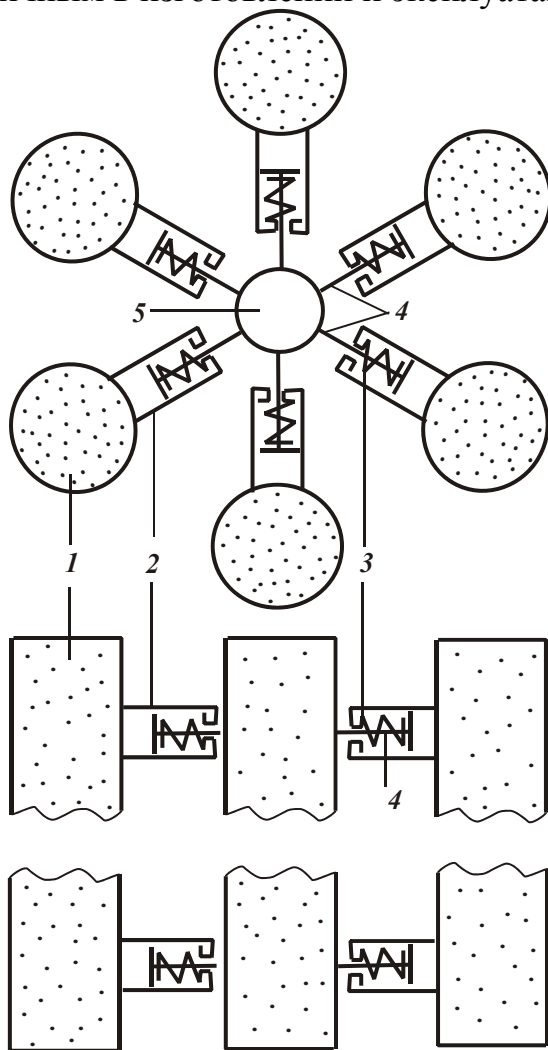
Инструмент для шлифования внутренних поверхностей: 1 - шлифовальный брусок; 2 - цилиндр; 3 - пружина; 4 - штырь (спица); 5 - вал.
